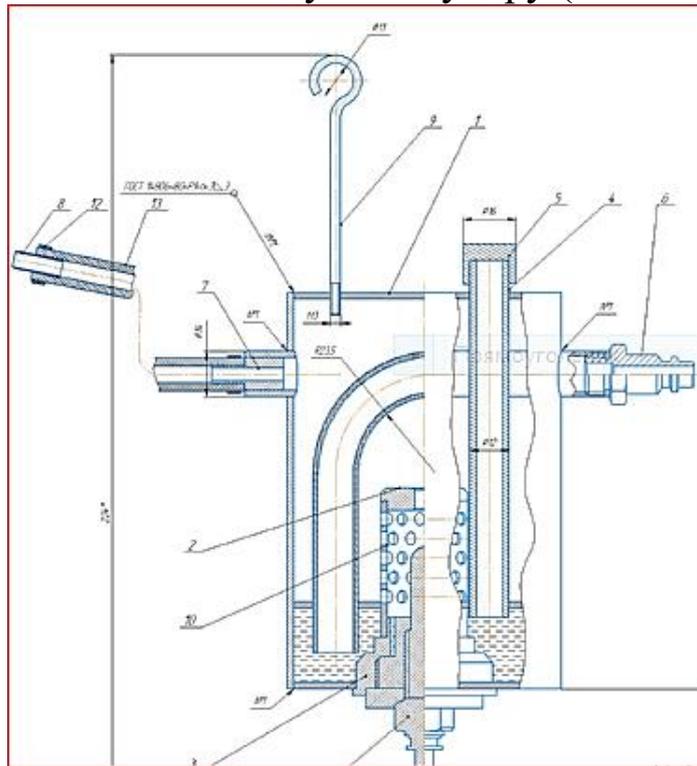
Приспособление для проверки герметичности подсоса воздуха в инжекторном двигателе
